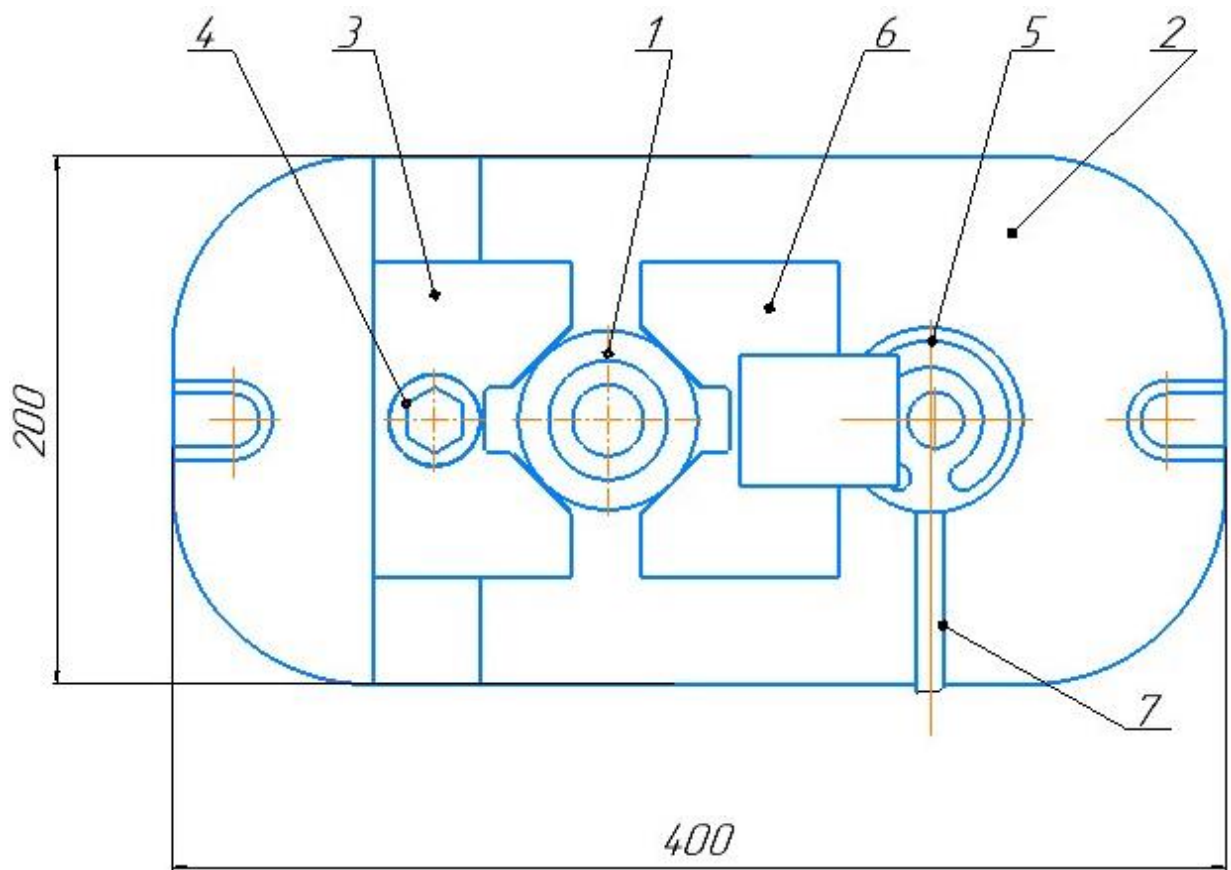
ескіз пристосування для обробки поперечного паза
